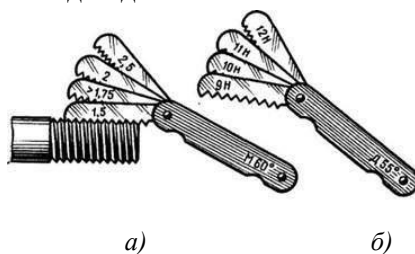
Резьбомер для измерения шага метрической резьбы (а) и дюймовой резьбы (б)
